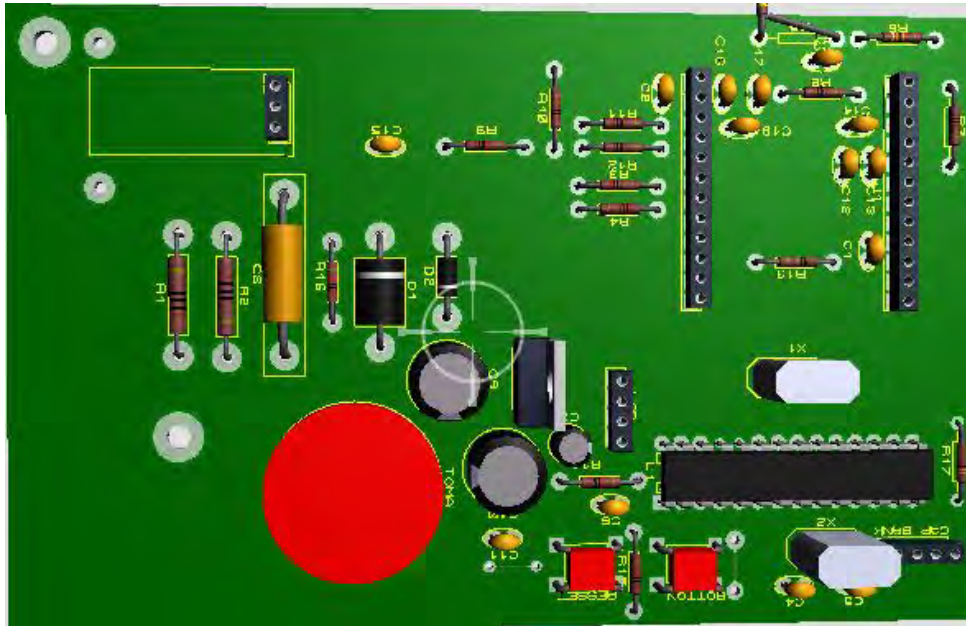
Diseño de la tarjeta de control del prototipo en Proteus 8
